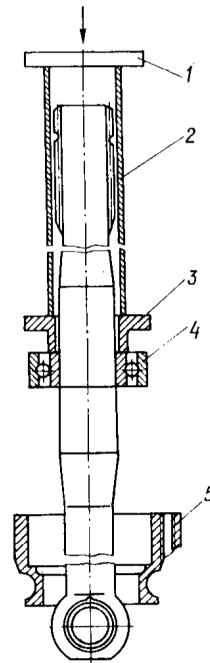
Оправка для напрессовки подшипника и грязезащитного кольца на полуось
